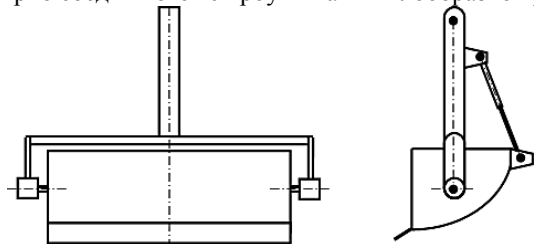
Схема поворотного ковша с вилообразной рукоятью
